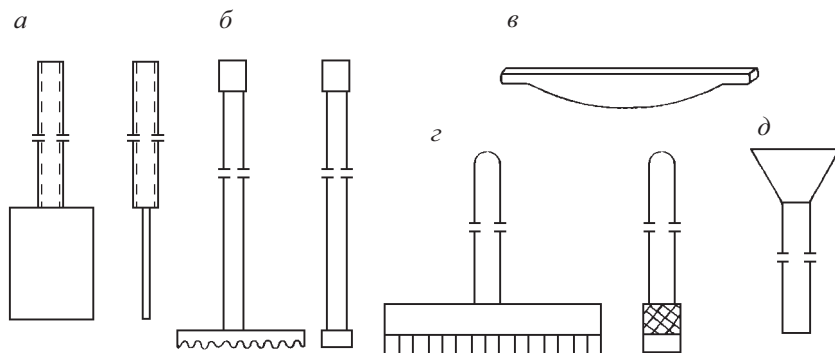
Приспособления и инструмент для выполнения футеровки:
